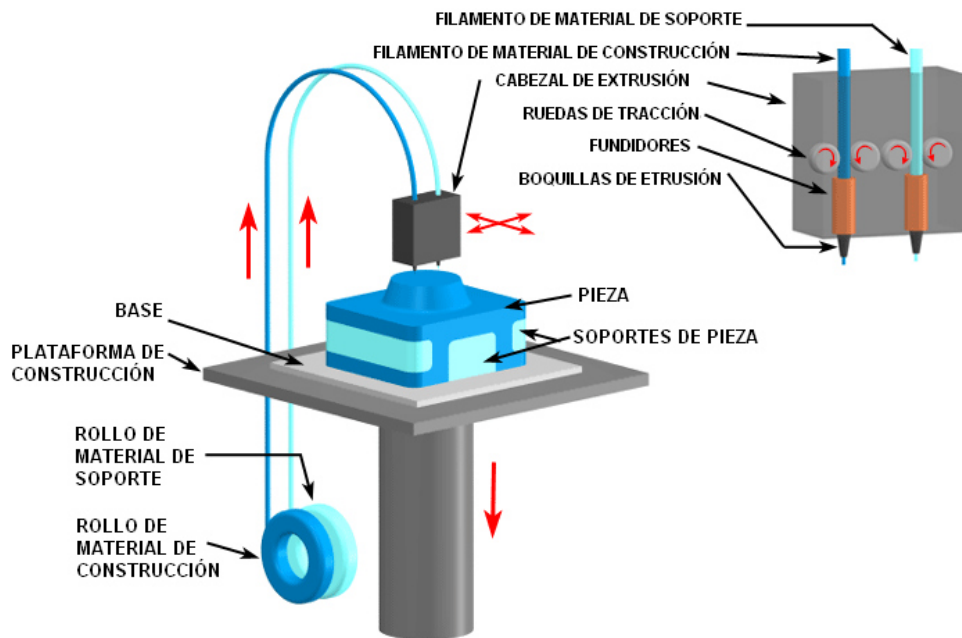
Partes principales y principio de operación del proceso de prototipado rápido por deposición de fundido.
